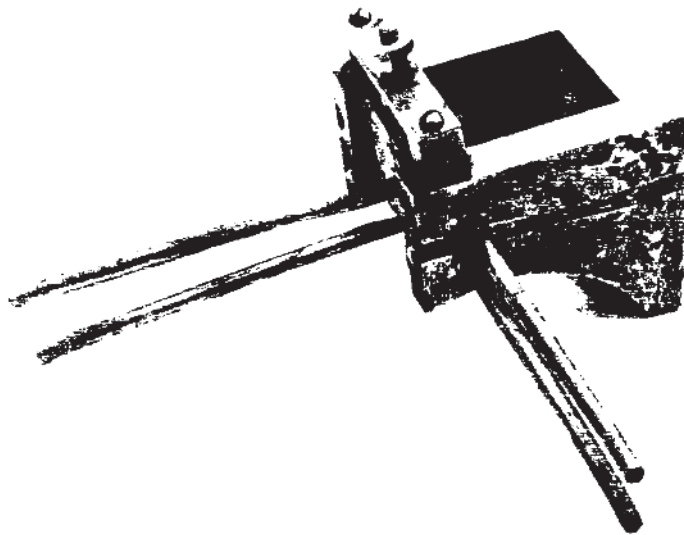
Внешний вид прямоугольного кристаллизатора для горизонтального электрошлакового упрочнения криволинейных поверхностей деталей
